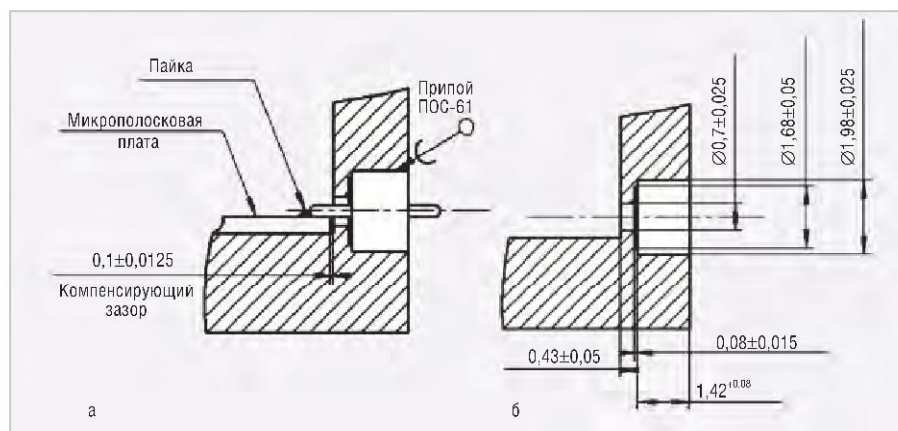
СВЧ-ввод МК100А: а) установка в корпус изделия; б) разделка корпуса под установку ввода
